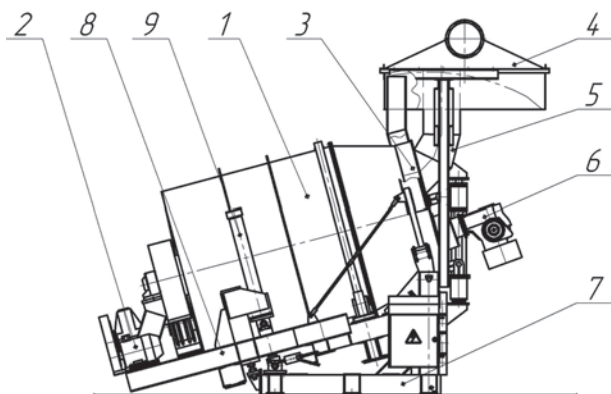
Общий вид ротационной наклоняющейся печи: 1 – корпус печи; 2 – привод; 3 – крышка поворотная; 4 – зонт; 5 – дымоход; 6 – горелка; 7 – рама опорная; 8 – рама поворотная; 9 – привод наклона печи
